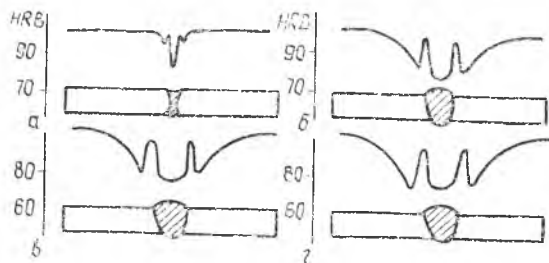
Изменение твердости металла зоны термического влияния при различных способах сварки плит толщиной 15 мм из термически упроченного сплава 1201 (*а* — электронно-лучевая сварка; *б* — сварка в гелии; *в* — плазменная сварка; *г* — аргонодуговая сварка)
